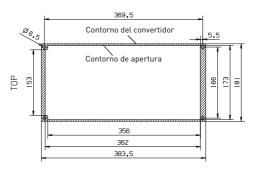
Dimensiones de corte del montaje con bridas para MI4 (Unidad: mm)
